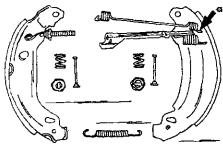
Детали разобранного тормоза Bendix. Подсоединить пружинный крюк, как показано на рисунке.
